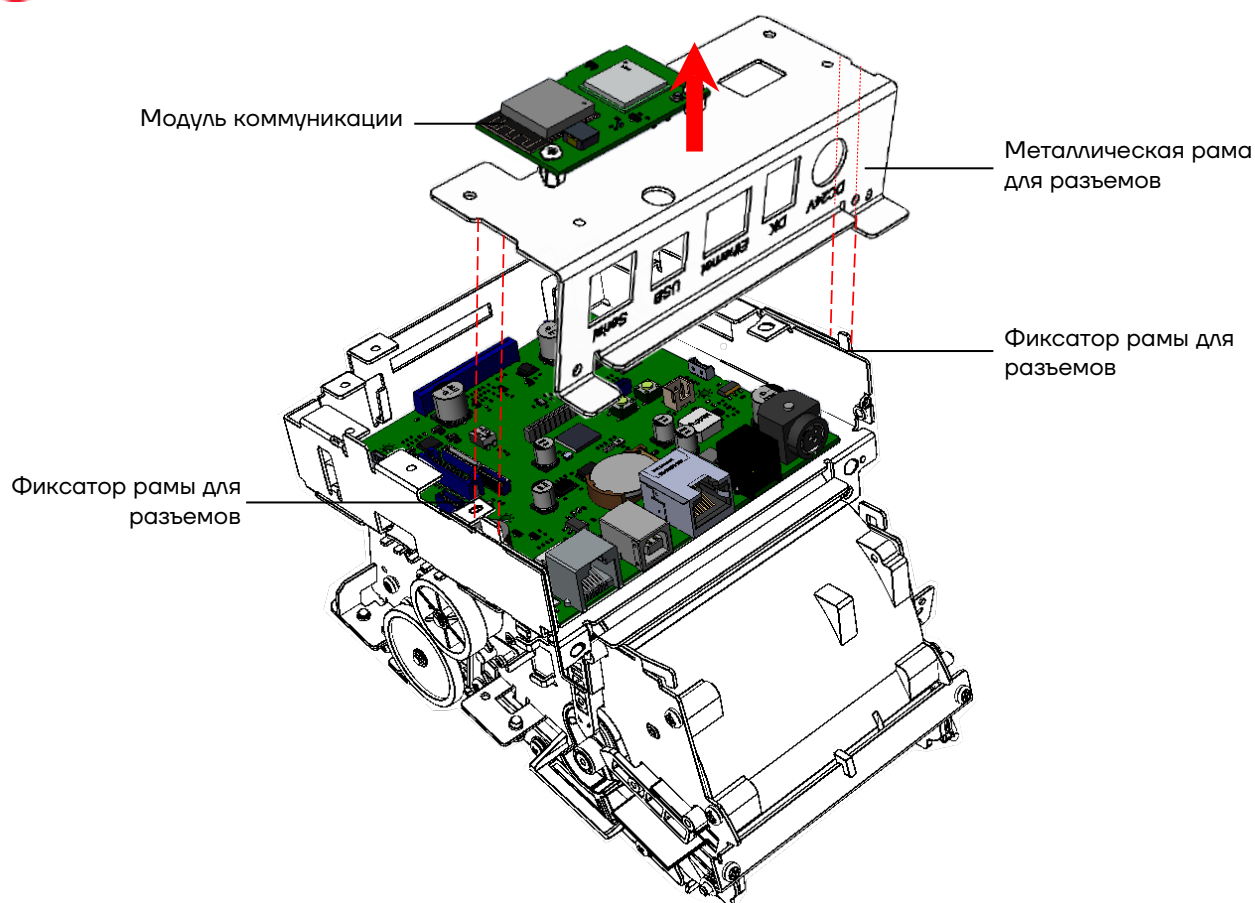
Отделение металлической планки от корпуса печатающего устройства
